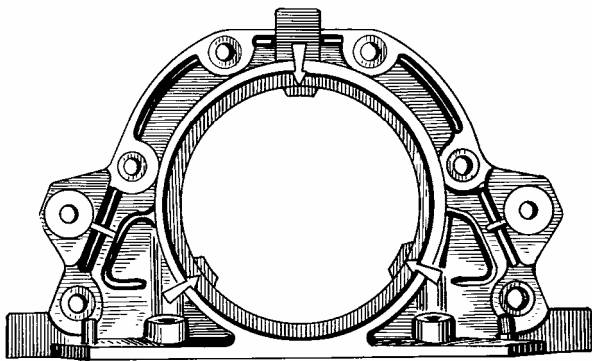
Держатель заднего сальника коленчатого вала.
